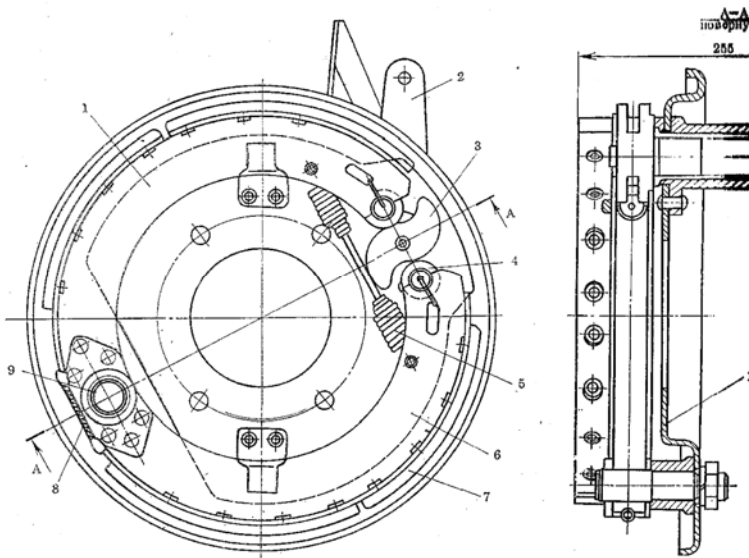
Барабанный тормозной механизм без усилителя:
